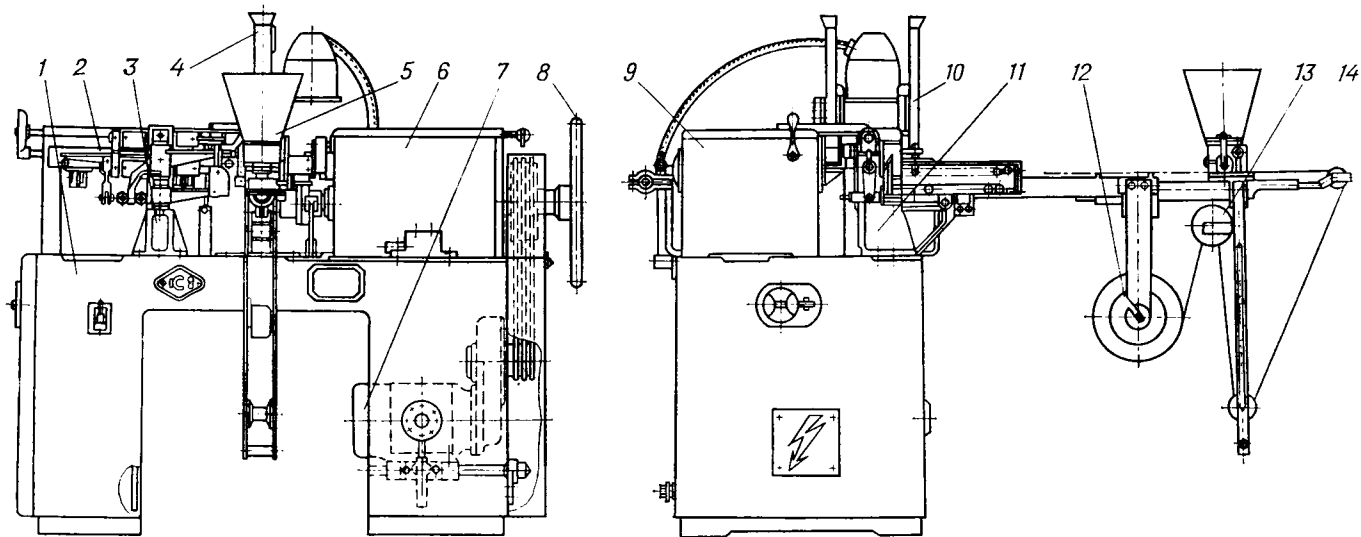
Схема коробкклеильного станка СпКВ-3:
